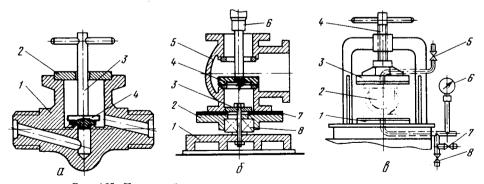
Приспособления для ремонта и испытания арматуры: a — для притирки вручную: I — корпус вентиля; 2 — центрующий диск; 3 — вороток; 4 — притир; 6 — для притирки механизированным способом: I — стол станка; 2 — диск установочный; 3 — шайба установочная; 4 — притир; 5 — корпус задвижки; 6 — шпиндель сверлильного станка; 7 — прокладка резиновая; 8 — шарикоподшипник;  $\theta$  — для испытания арматуры: I — диск упорный нижний с прокладкой; 2 — вентиль; 3 — диск упорный подвижной с прокладкой; 4 — винт; 5 — вентиль для выпуска воздуха; 6 — манометр; 7 — вентиль подачи воды (воздуха); 8 — вентиль выпуска воды (воздуха)
